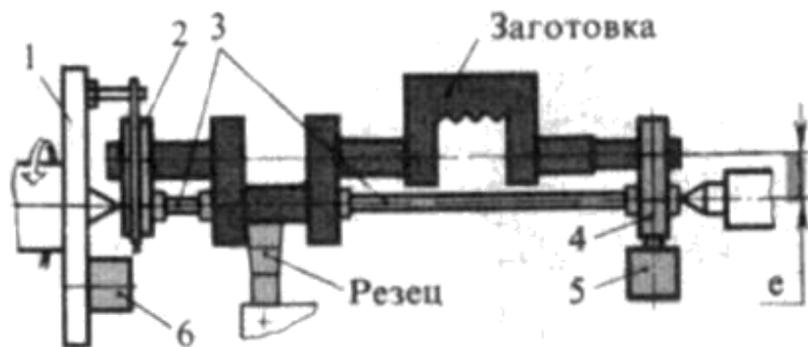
Обработка коленчатого вала в центросместительных шайбах:
